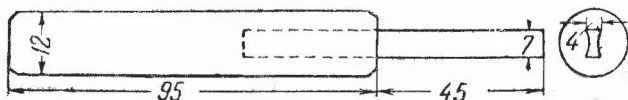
Детали для крепления провода при оборудовании внутридомовой проводки.
